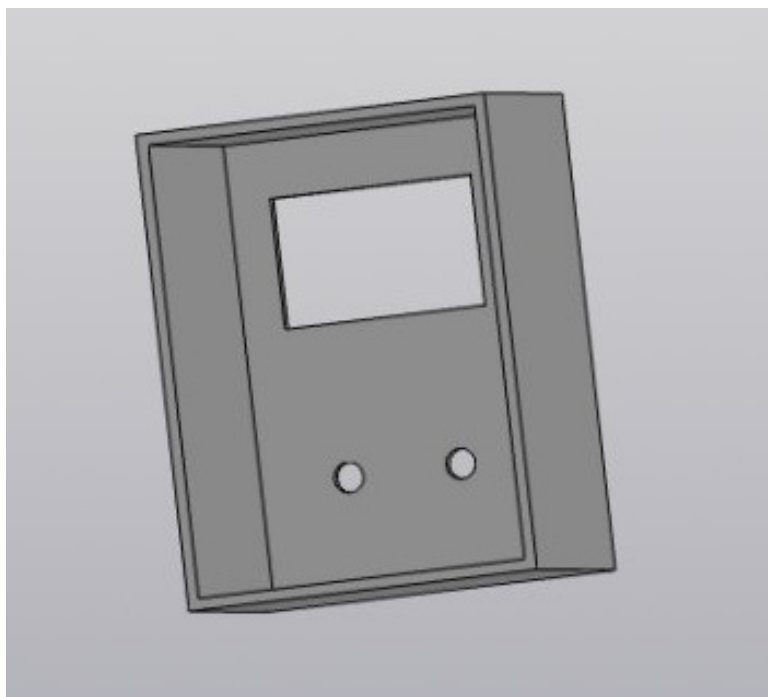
Основна частина корпусу пристрою, вигляд ззаду.
